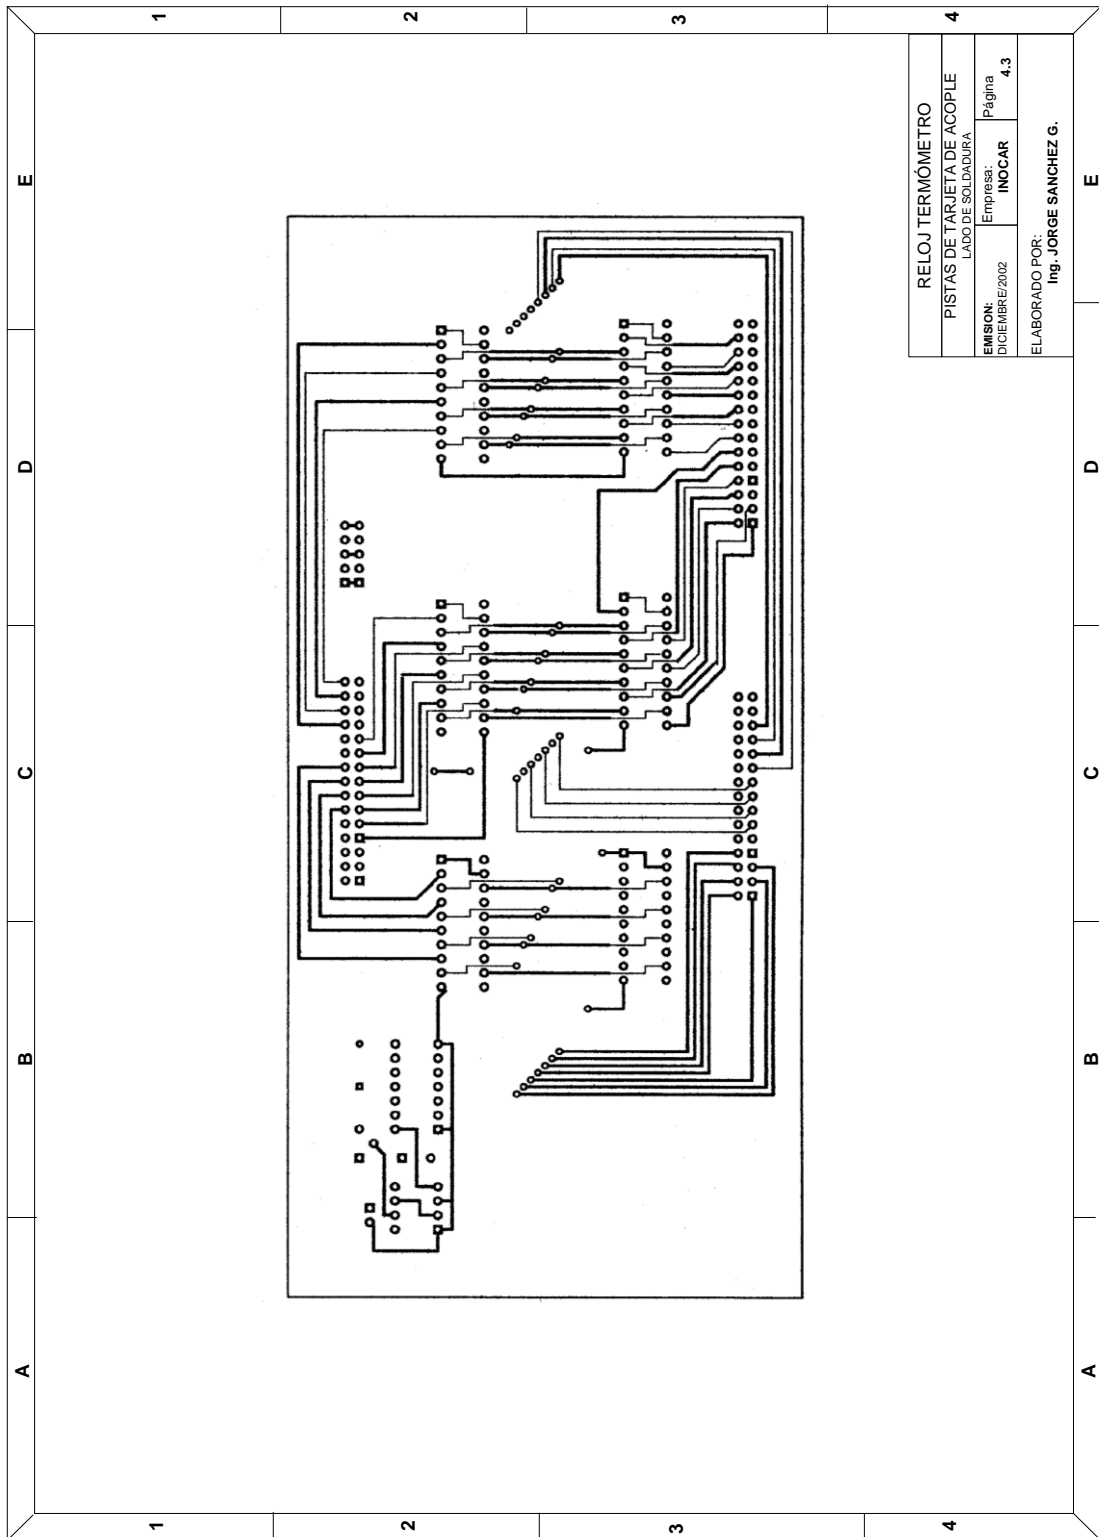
Tarjeta de acople (Pistas lado de soldadura)
